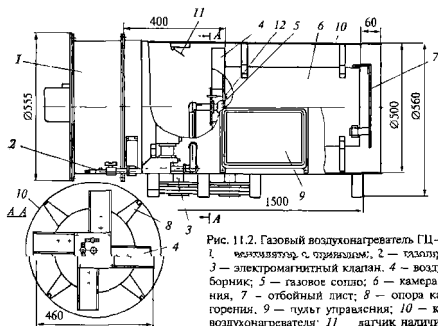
Газовый воздухонагреватель ГЦ-100.
